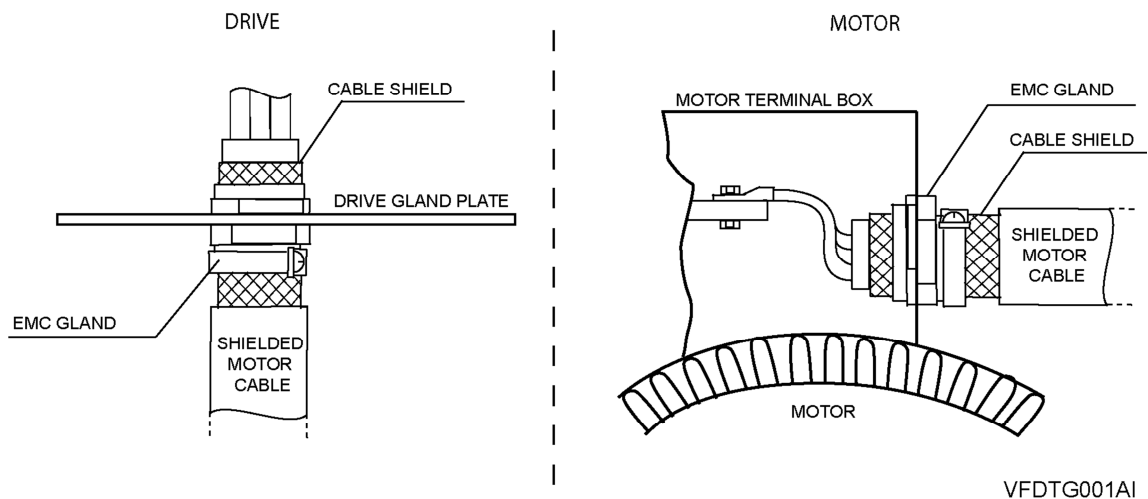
Richtiger Anschluss des Motorkabels
